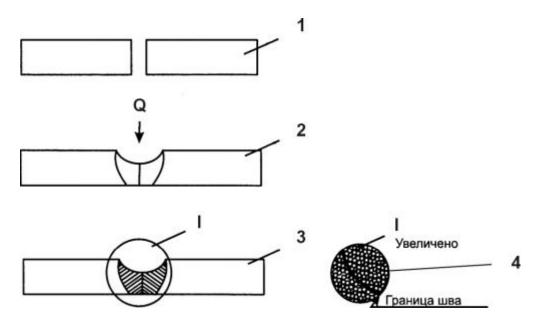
Схема стадий образования соединения сваркой плавлением:
